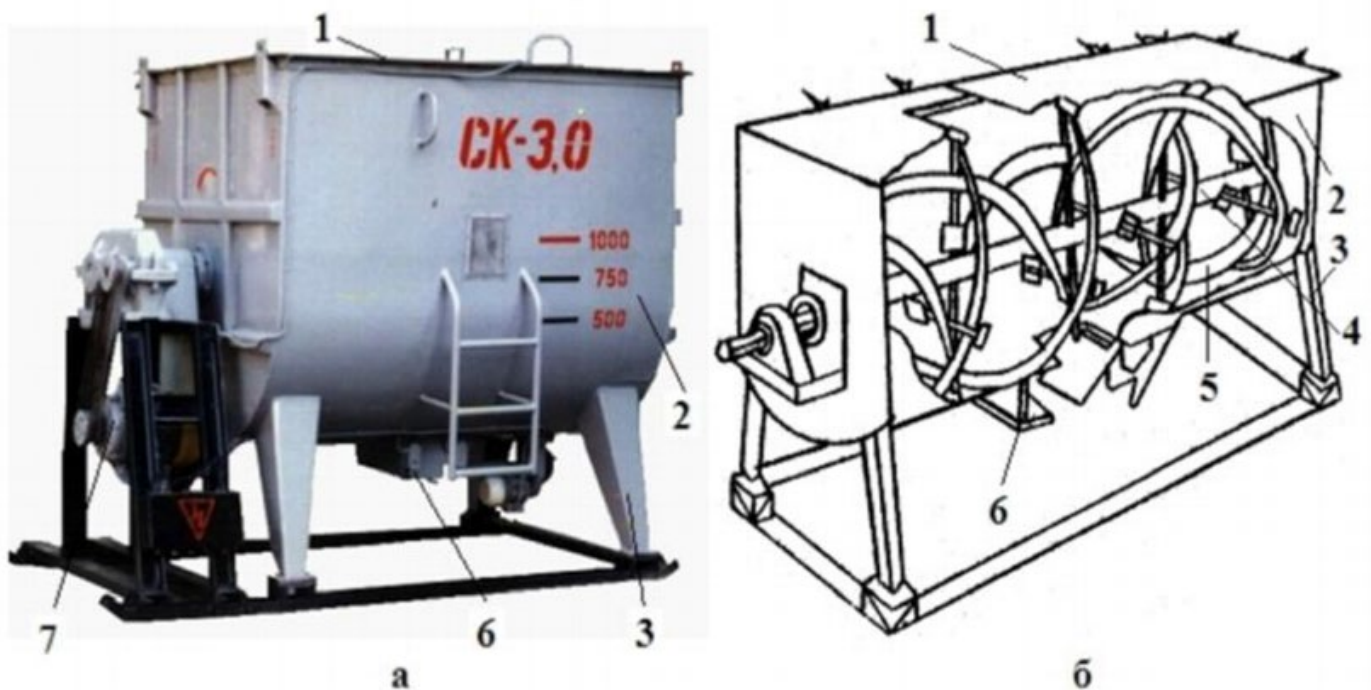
Загальний вигляд і схема горизонтального змішувача кормів СК-3.0: 1 – кришка; 2 – корпус зі змішувальною камерою; 3 – рама; 4 – вал із стрічковою навивкою (шпек); 5 – лопаті вала; 6 – вивантажувальне вікно; 7 – електропривід.
